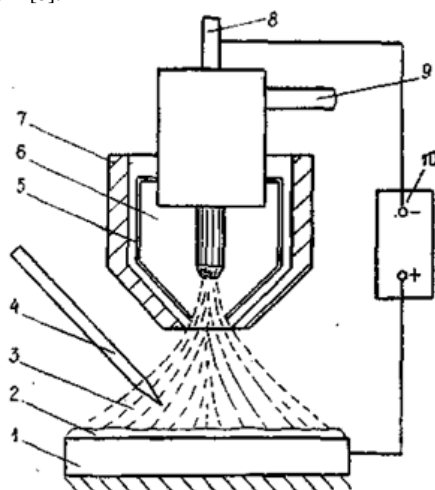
Схема плазменной наплавки: 1 – изделие; 2 – наплавка; 3 – плазменная струя; 4 – присадочный материал; 5 – сопло, формирующее плазменную струю; 6 – защитный газ; 7 – сопла для защитного газа; 8 – вольфрамовый электрод; 9 – охлаждающая вода; 10 – источник питания
